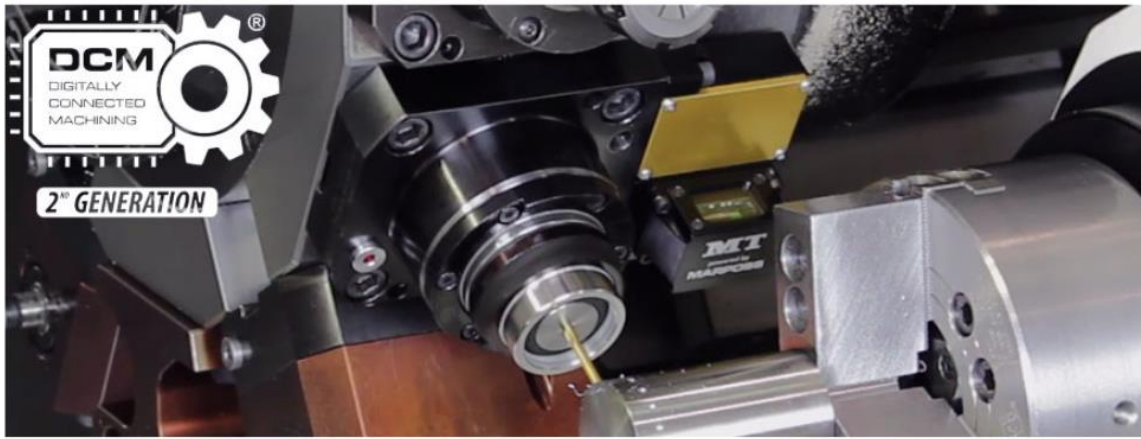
Приводний блок MT-DCY Digitally Connected Machining
